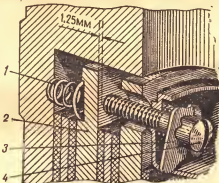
Регулировка хода среднего ведущего диска: 1 — отжимная пружина; 2 — ведущий диск; 3 — стопорная шайба; 4 — регулировочный винт.
